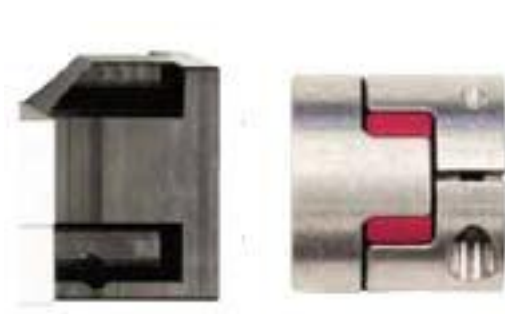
Flange MF2040-Nema 23 e acoplamento do motor [43].
